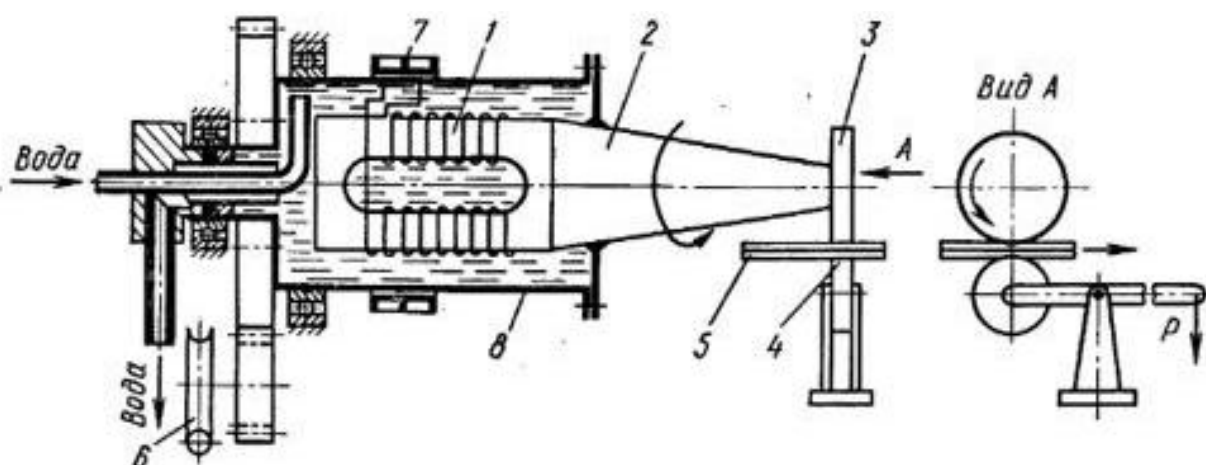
Схема установки для роликовой сварки ультразвуком: 1 — электромеханический преобразователь; 2 — трансформатор упругих колебаний; 3 — сваривающий ролик; 4 — прижимной ролик; 5 — изделие; 6 — механизм привода; 7 — подвод тока от ультразвукового генератора; 8 — кожух преобразователя.
